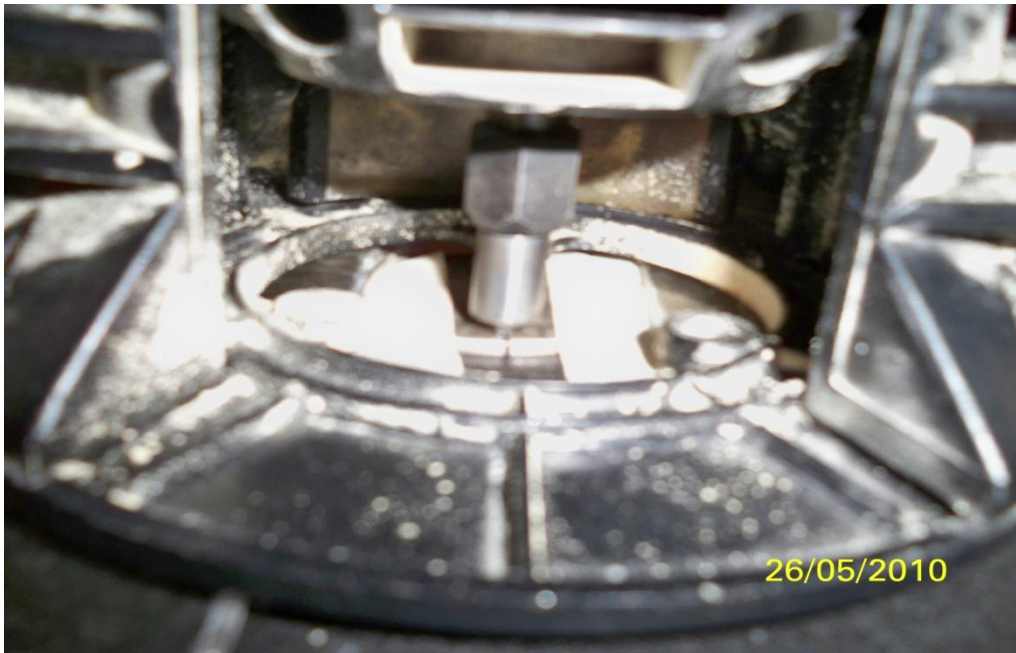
Inicio del proceso de soldado en placas de acrílico
